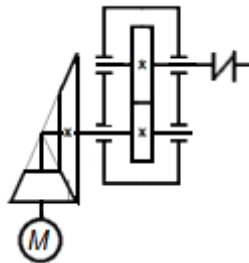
Кинематическая схема привода с открытой конической зубчатой передачей
